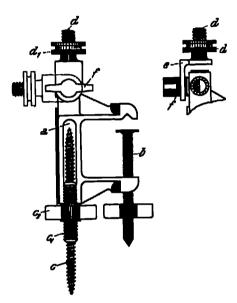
Hilfsstativ mit Baumschraube. a Hauptkirper aus Leichtmetall mit Schraube b zum Festklemmen des Stativs en einer Tischplatte o del. sowie Schraube mit Holsgewinde e, Metollgewinde e, und Flügelmutter e_s. Das Stativgswinde d mit Rändelring d₁ ist am umlegbaren Winkelstück e befestigt, das in seiner jeweiligem Stellung durch die Klemmschraube f festgehelten wird; damit ist such die Lage der Kamera fixiert
